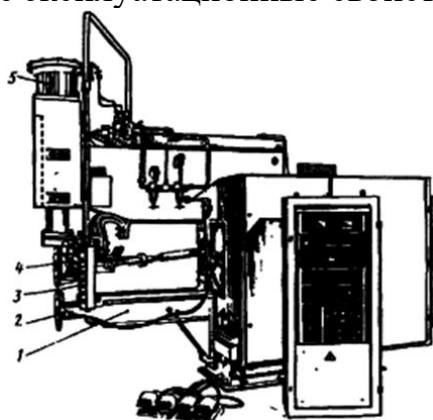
Машина шовной сварки постоянного тока МШВ-7501
